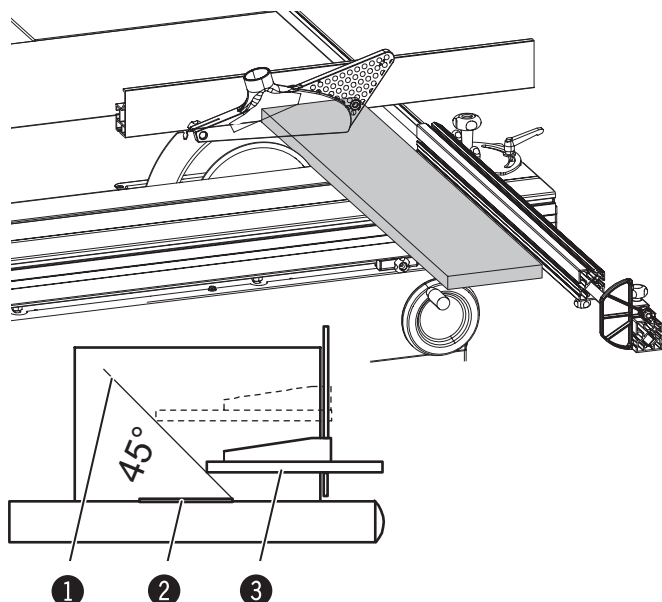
Cortes longitudinales con la regla de corte paralelo
